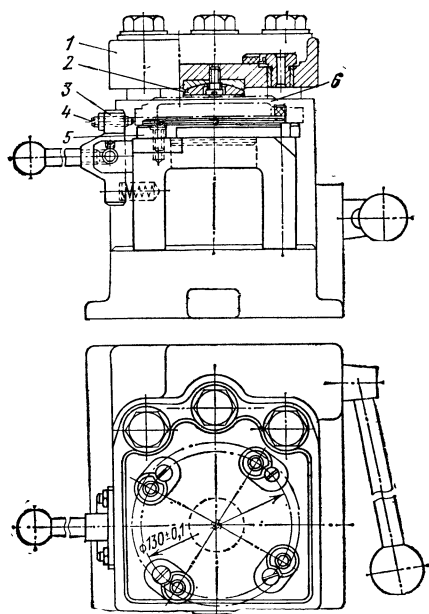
Компоновка скальчатого кондуктора для обработки четырех отверстий в круглой крышке
